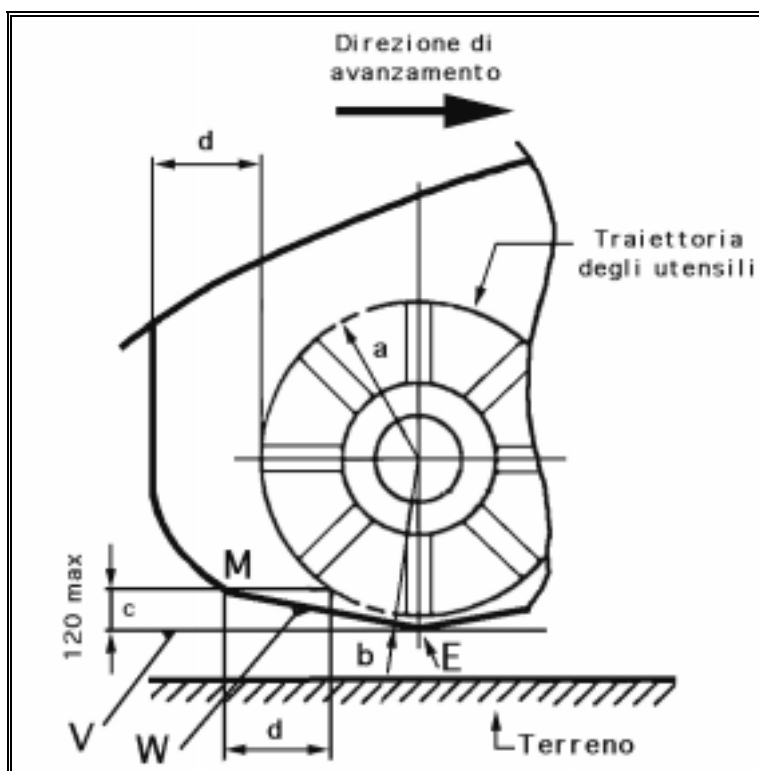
Dispositivo di condizionamento - Protezione laterale verso la parte posteriore della macchina
